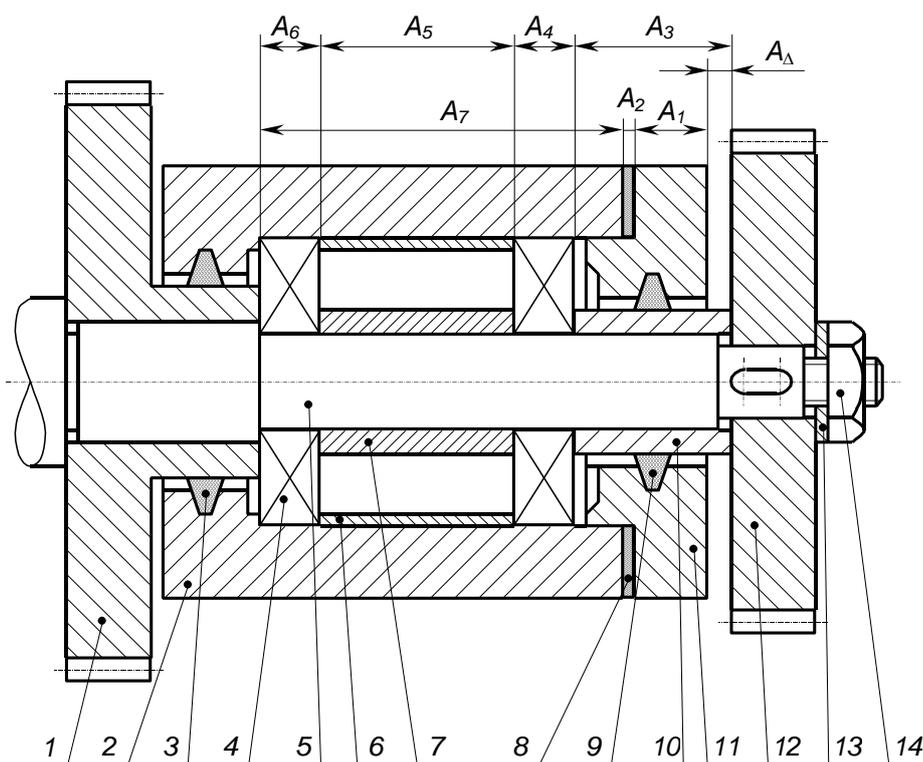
Часть сборочного чертежа механизма:
